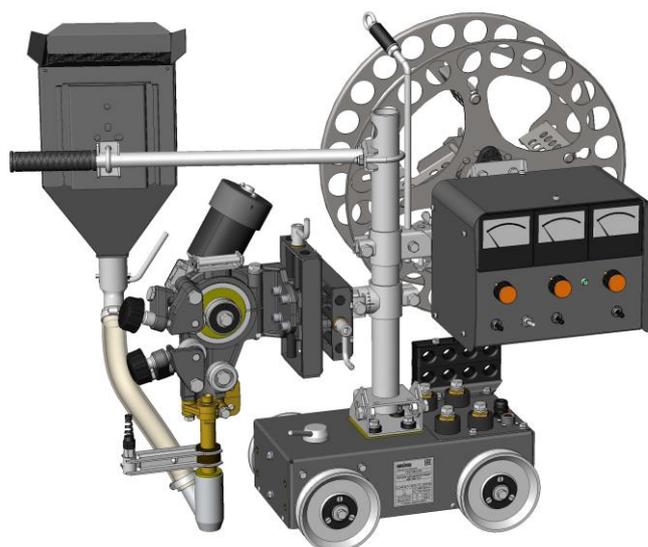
Автомат сварочный АДФ-1000-А исп.01
